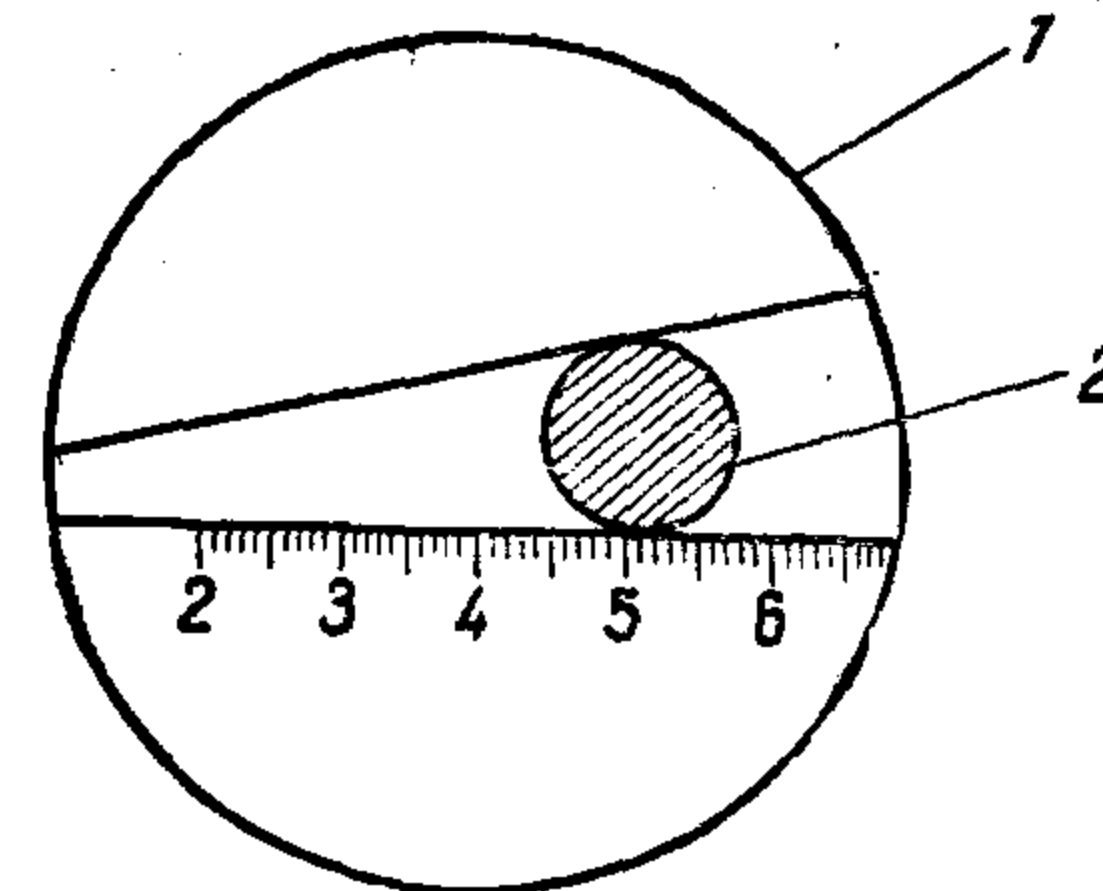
Прозрачный шаблон для измерения отпечатка:
